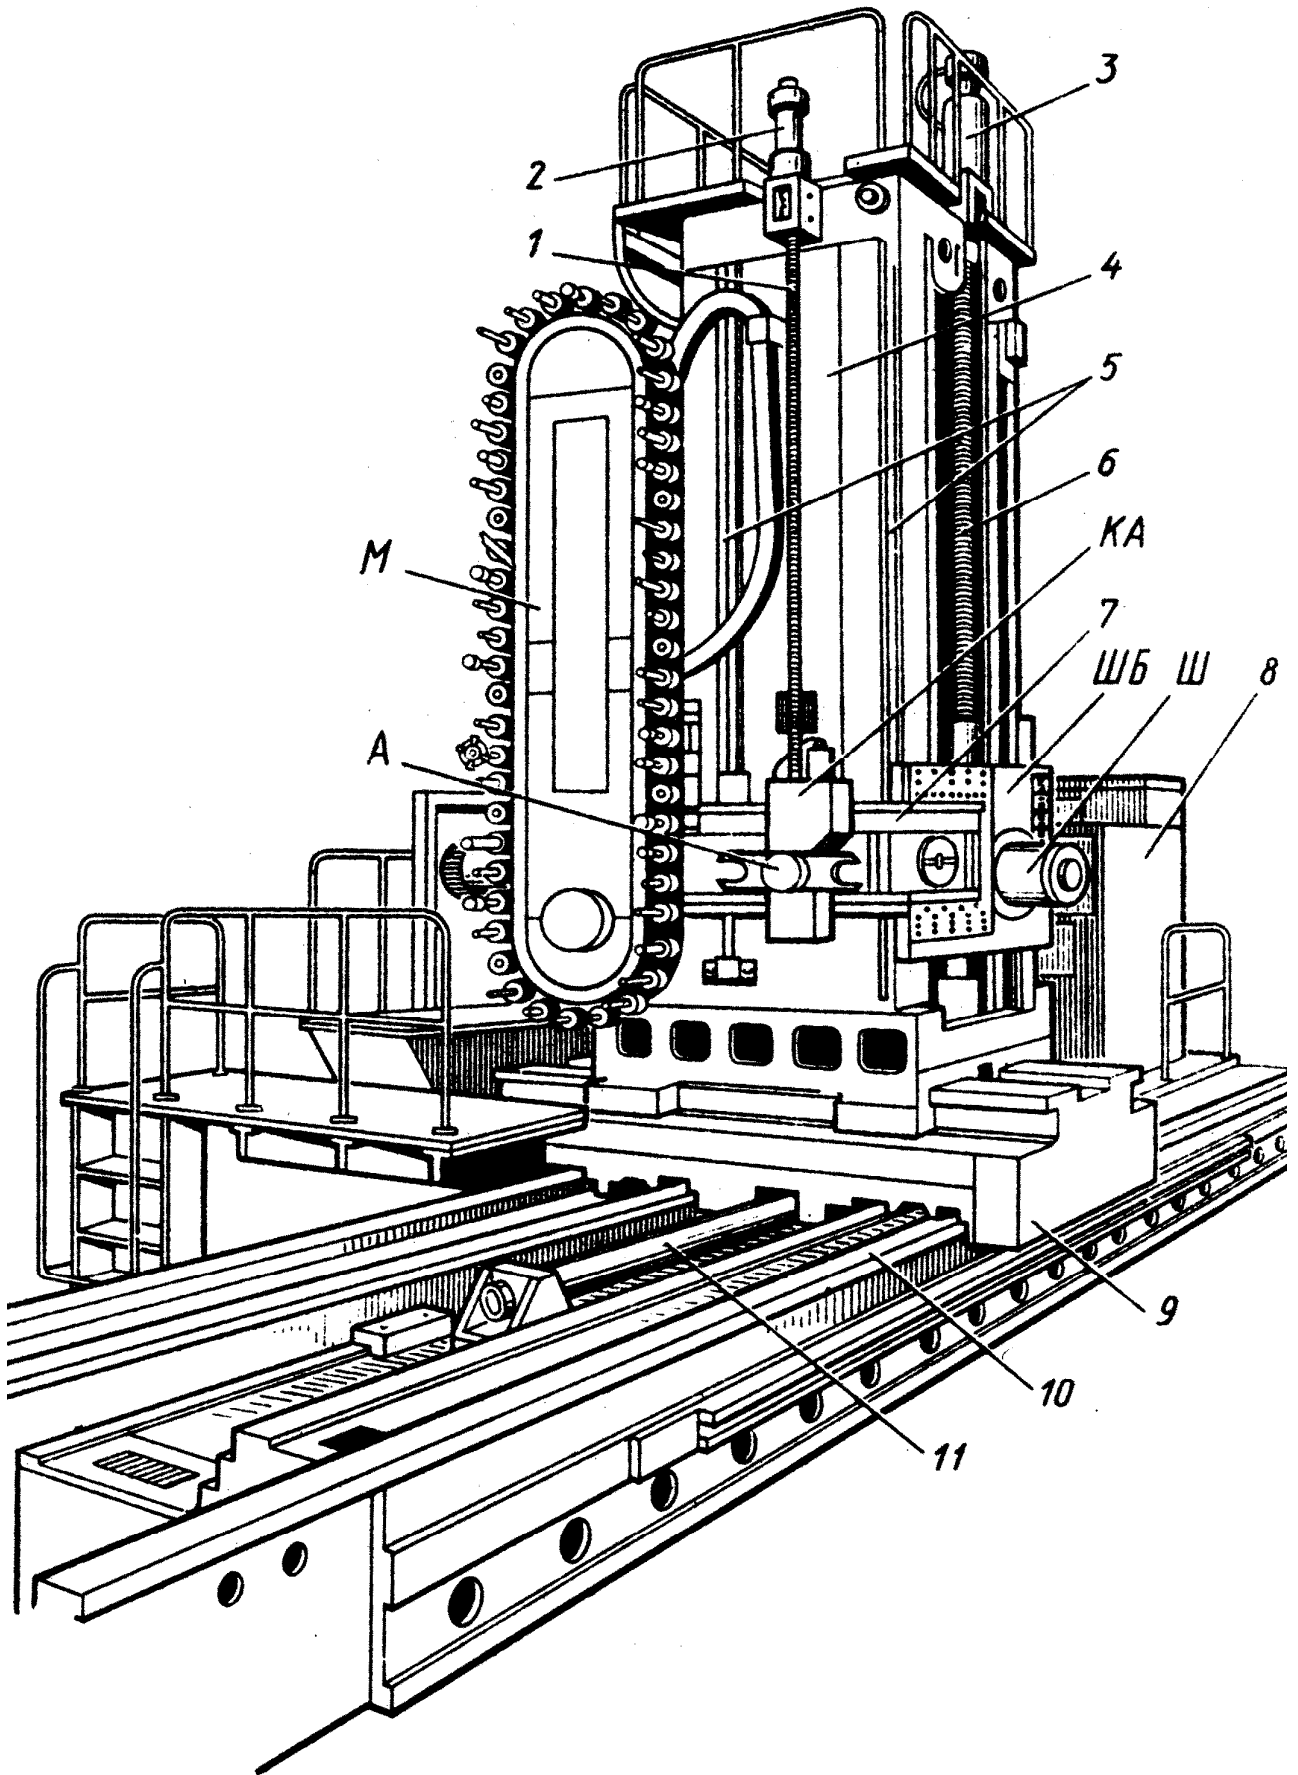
Багатоопераційний верстат IP1600MФ4
